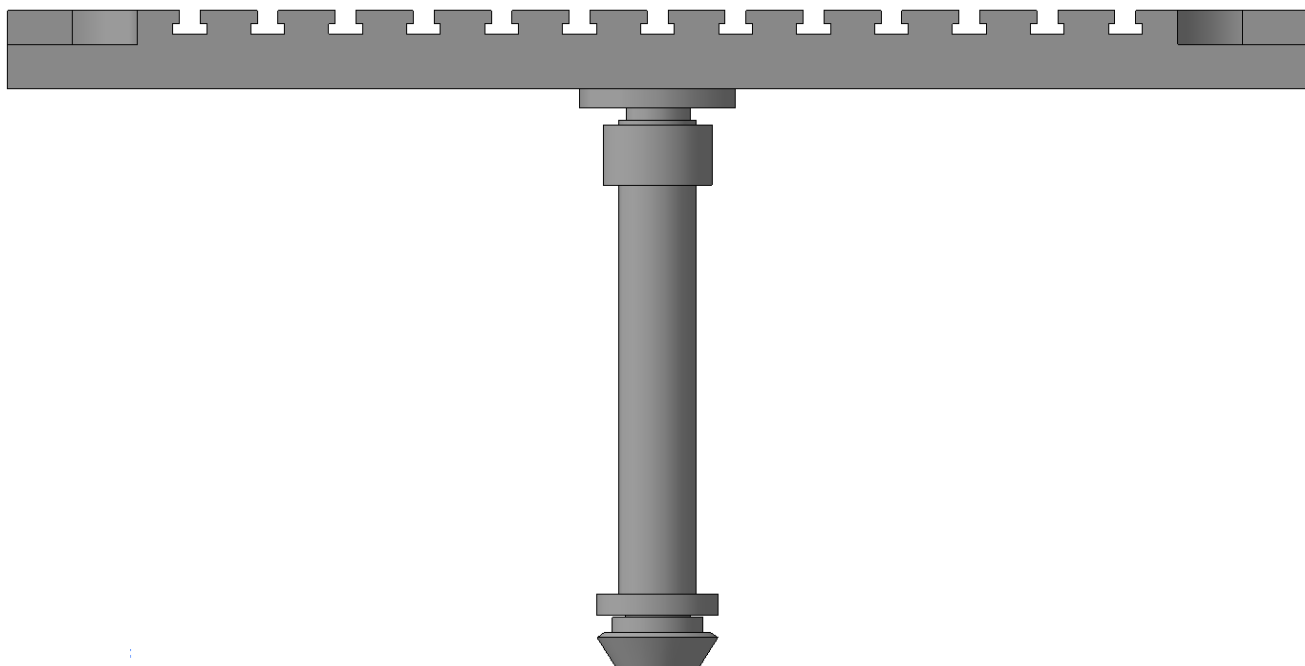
Вал ведомый в сборе с плитой и подшипниками
